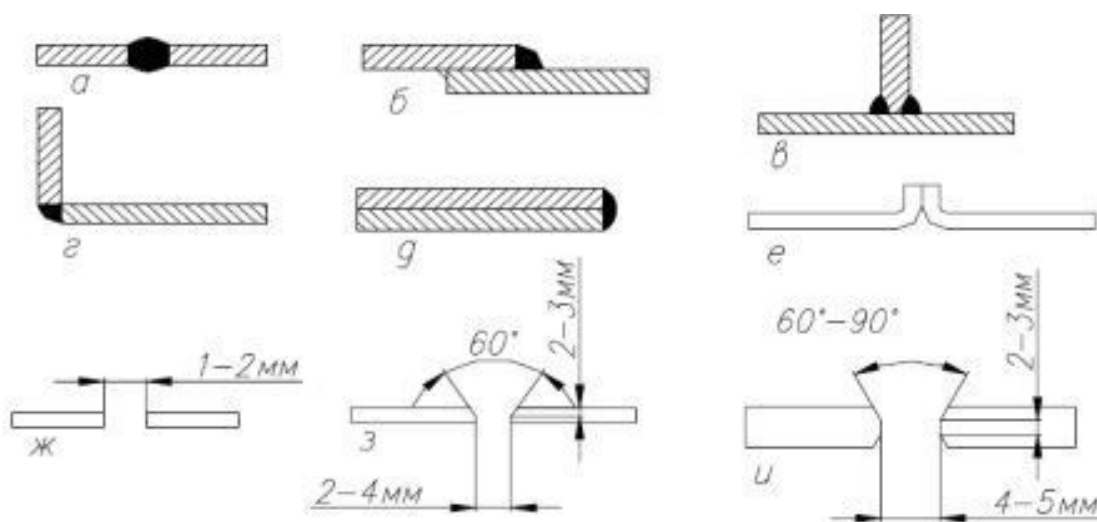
Типы сварных соединений (а-д) и подготовка кромок шва (е-и):
